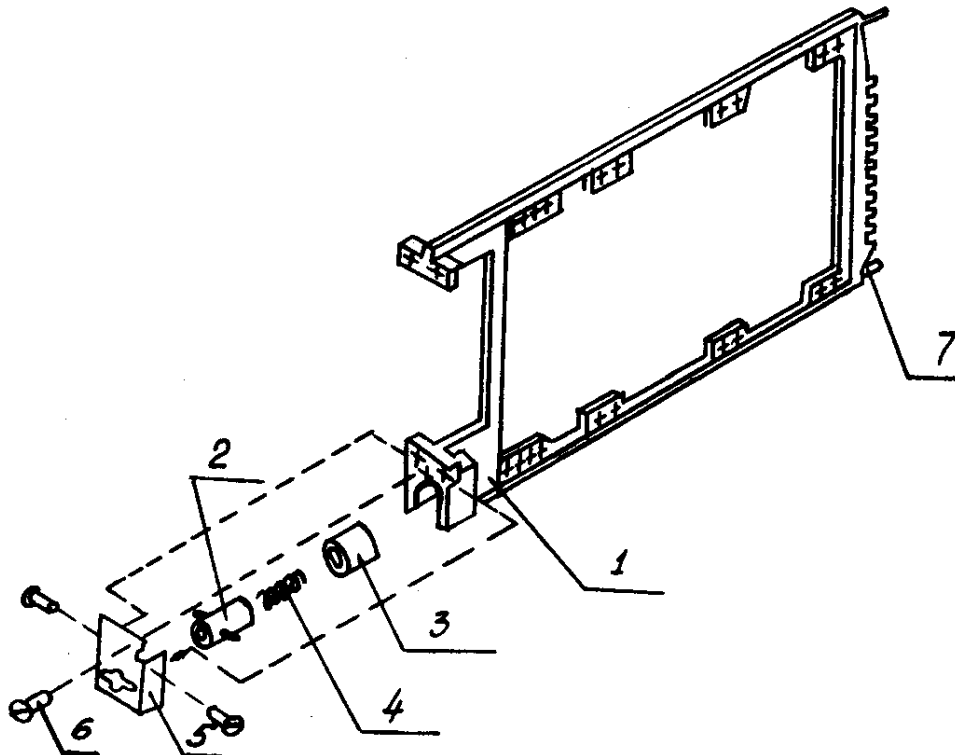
Рамка кассеты: 1 - рама; 2 - затвор; 3 - кулачок; 4 - пружина; 5 - планка; 6 - винт М3х6; 7 - ловитель
